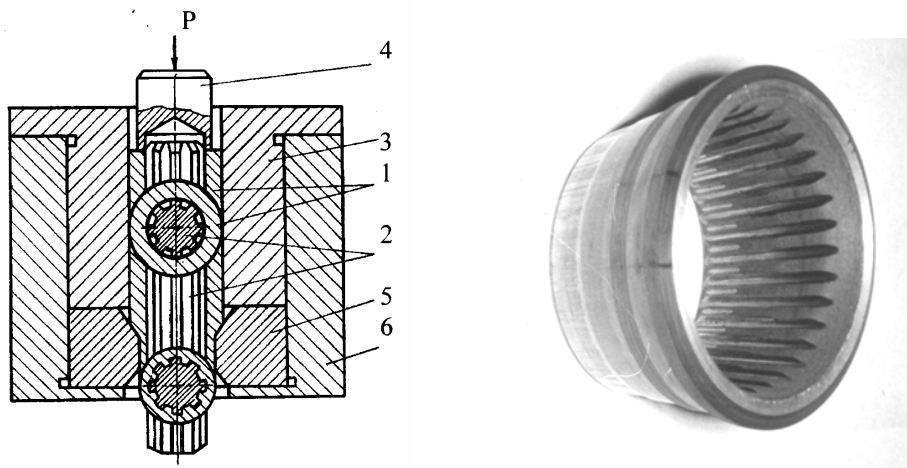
Схема формування внутрішніх шліців у трубній заготовці шліцьового з'єднання карданного вала дизель-поїзда ДП-2
